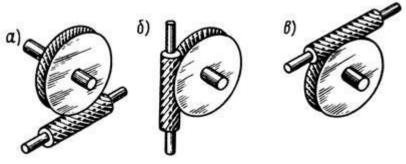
Расположение червяка относительно колеса: a — верхнее, δ — боковое, ϵ — нижнее
